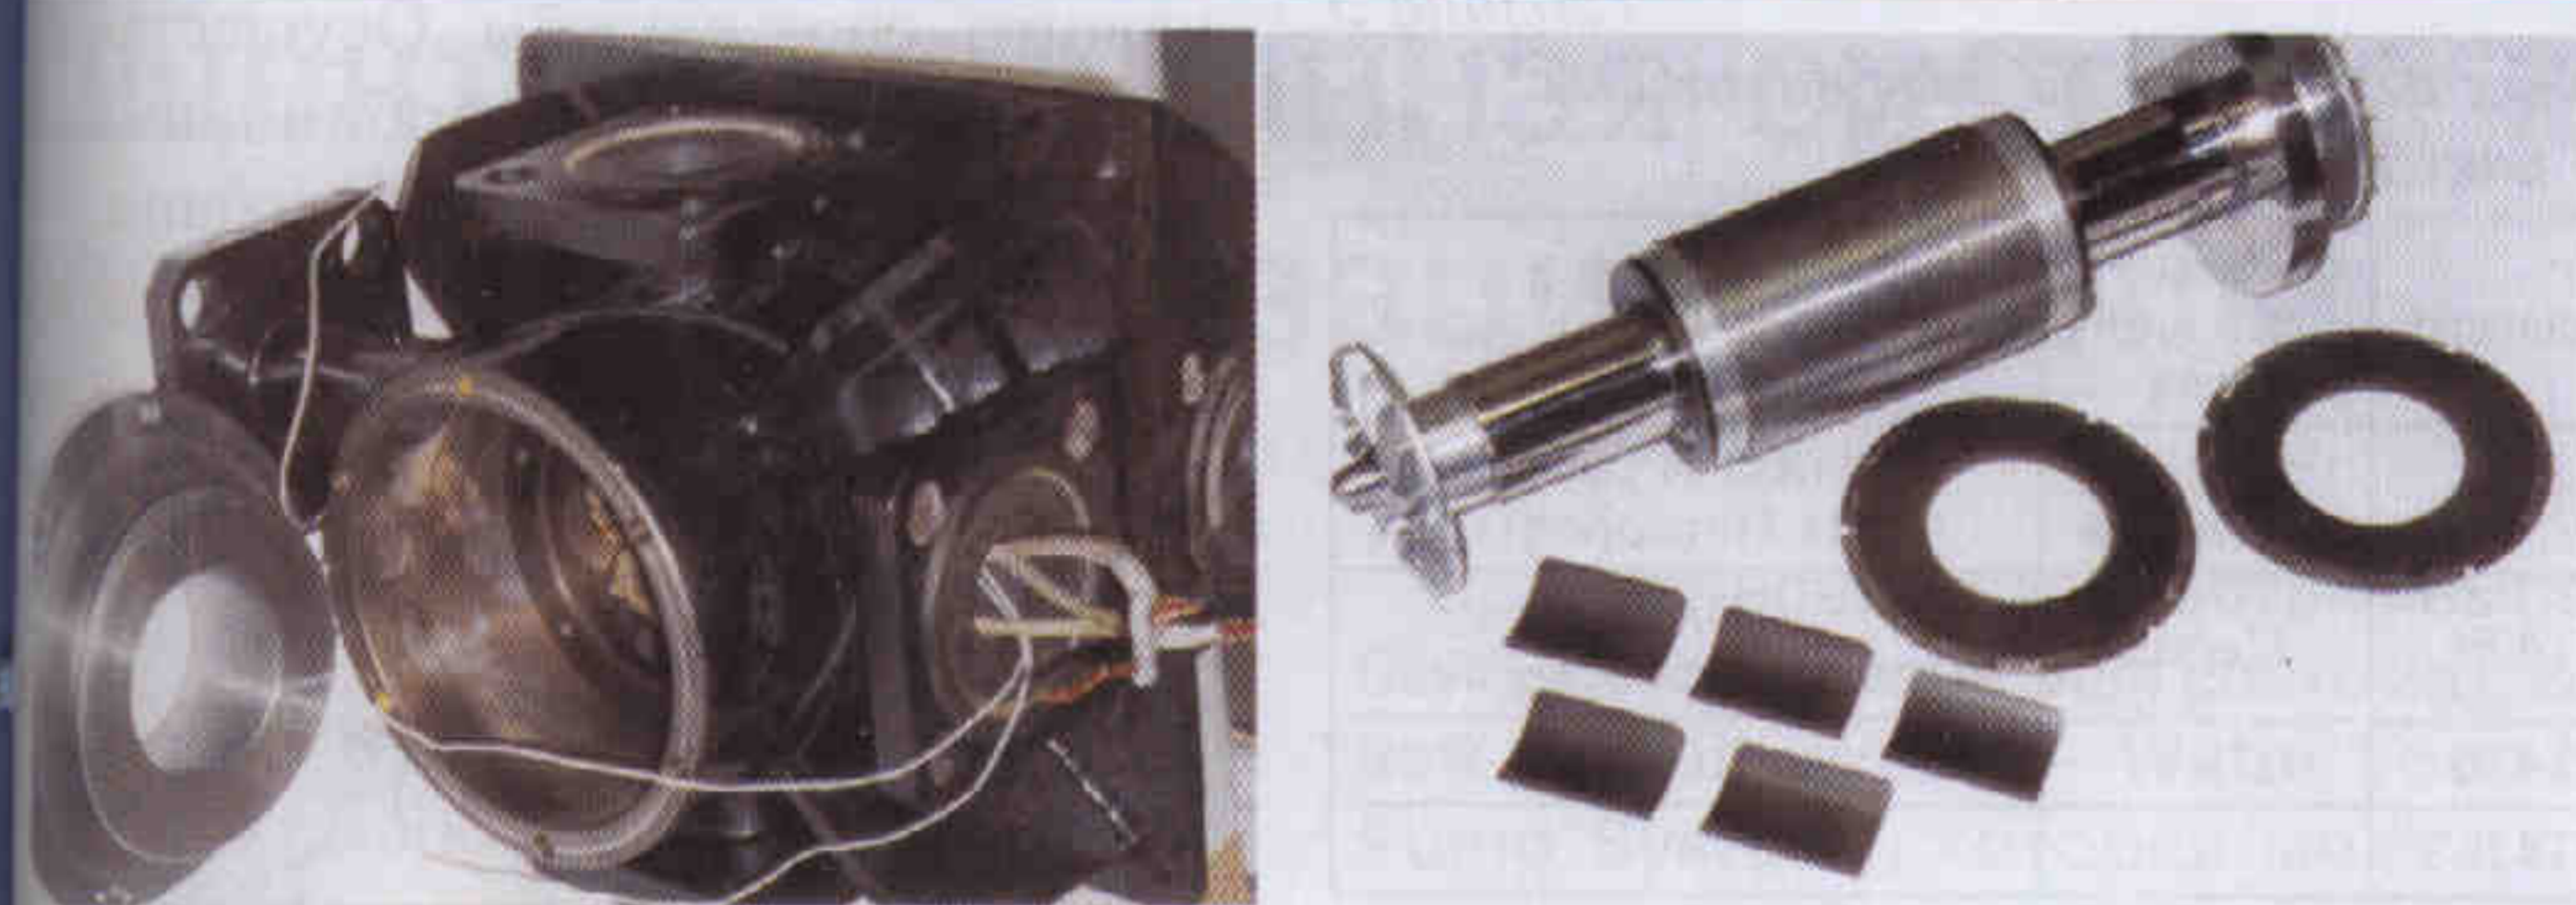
Корпус и ротор турбокомпрессора ТК-0,03
